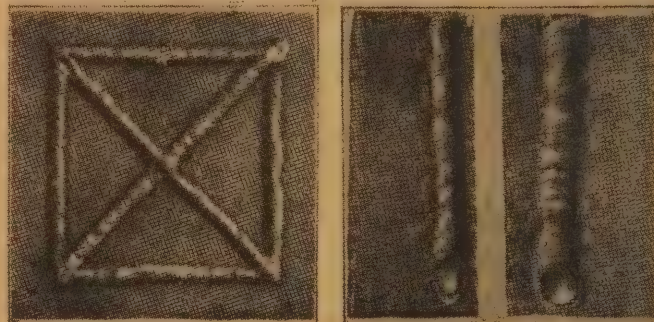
bis 5. Übungen für den Schweißer, Einhalten bestimmter Richtungen und Materiendielen.
